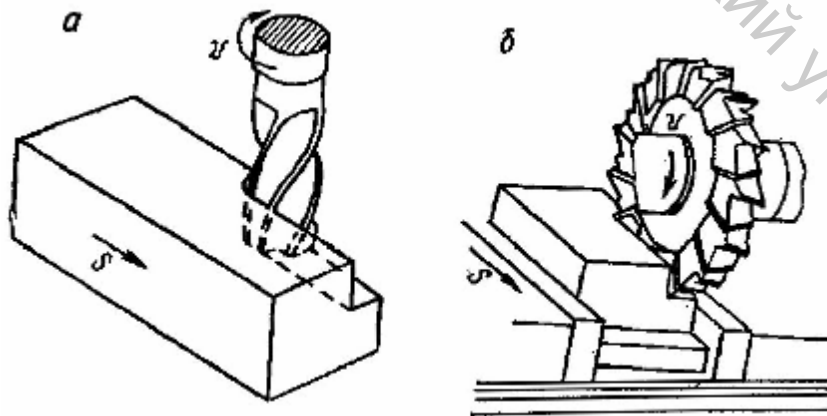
Схемы фрезерования уступов концевой и дисковой фрезами
